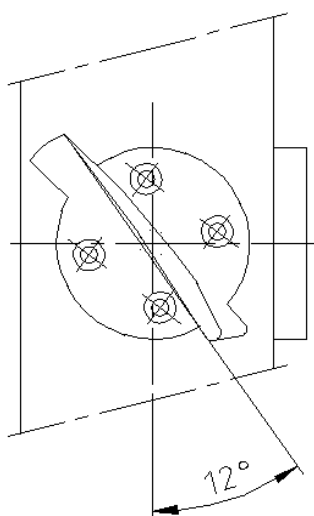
Regolazione dell'inclinazione palare per giranti con calotta in acciaio.
